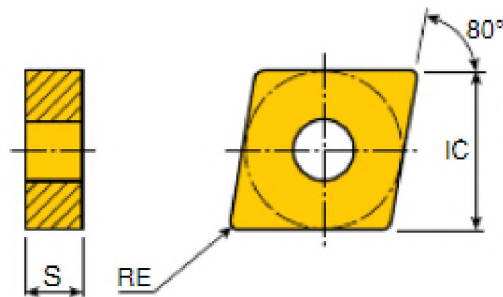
Пластина CNGG-090408ML .PVD покриття : TT5080
